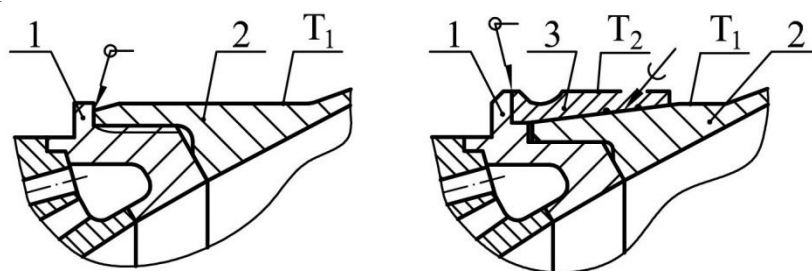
Конструкция соединения сопловой насадки с охлаждаемым корпусом камеры:
